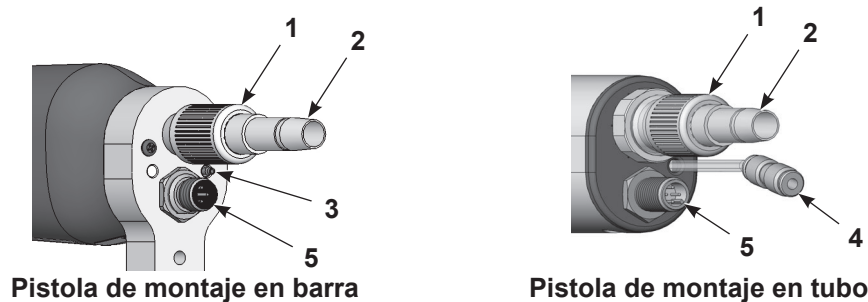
Conexiones de pistola - Pistolas de montaje en barra y en tubo
